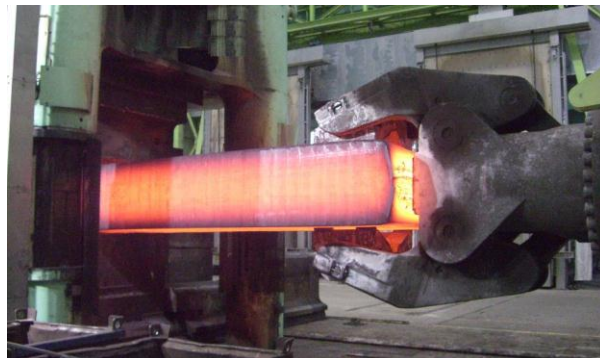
Ковка широкой заготовки, после которой заготовка находится близко к своей конечной геометрии
